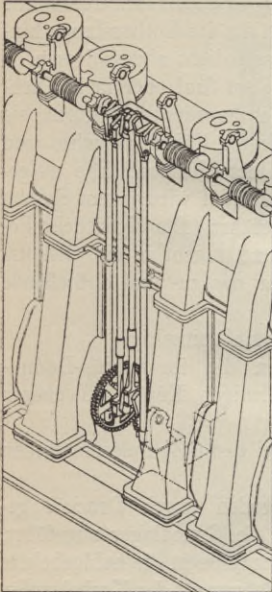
Steuerwellenantrieb der unsteuerbaren Sechszylinder-Viertakt-Schiffsdieselmachine der Deutschen Werke, Kiel.
